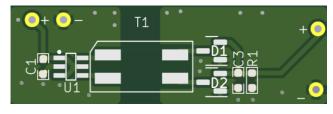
PCB 示意图(尺寸: 10.8 x 34.6mm)
